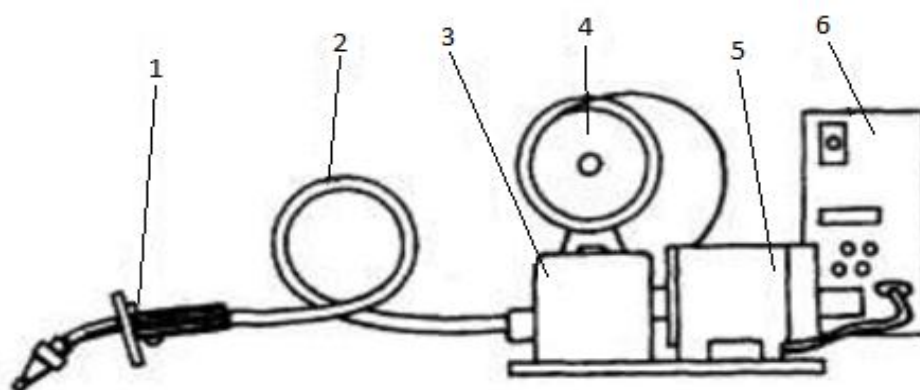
Схема полуавтомата для дуговой сварки:
